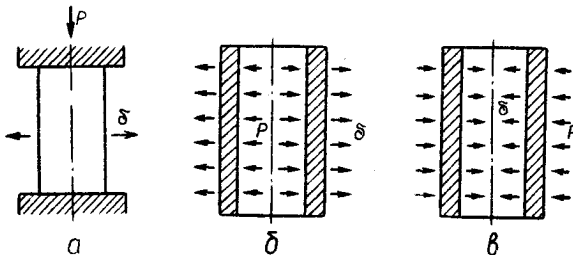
Схеми видів обробки деталей тиском: а — осадка; б — роздавання; в — обтискування
